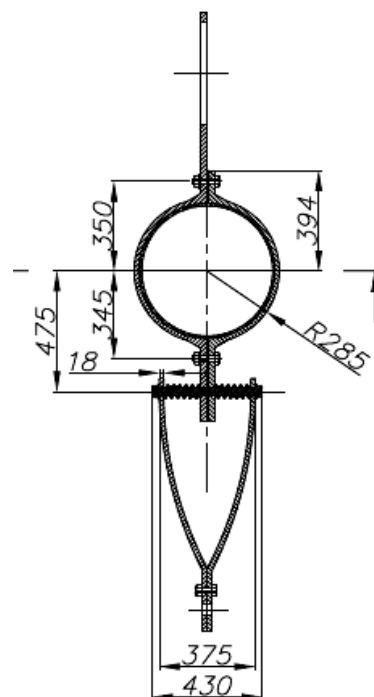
Устройство соединения троса с гибким трубопроводом (хомутом).
